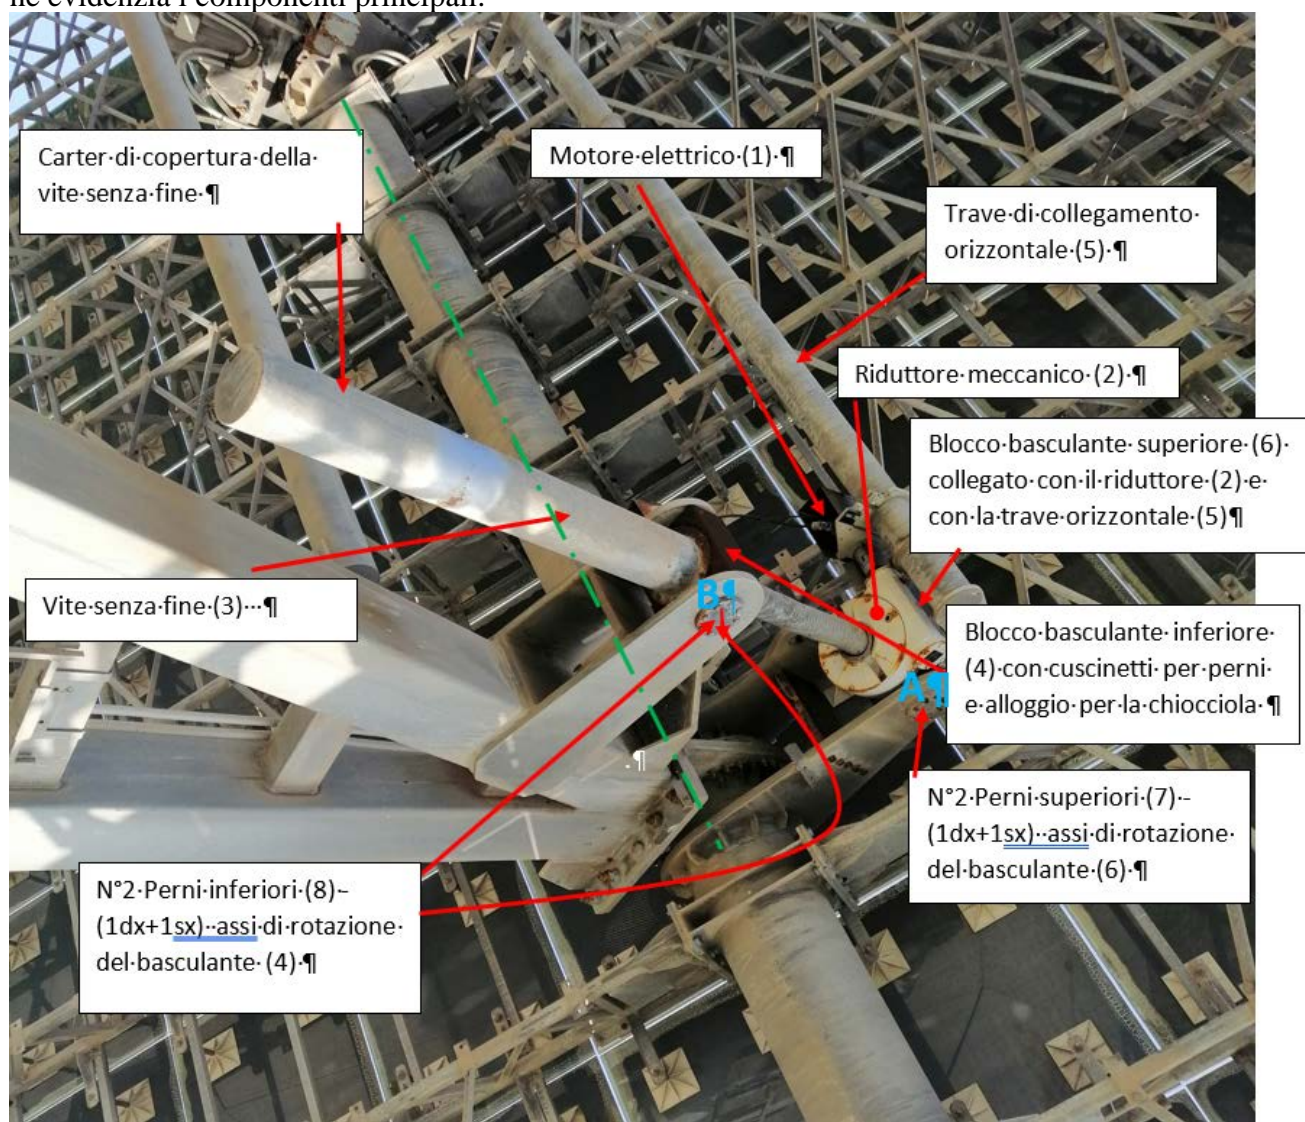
Vista del sistema di movimentazione in elevazione dell'eliostato
